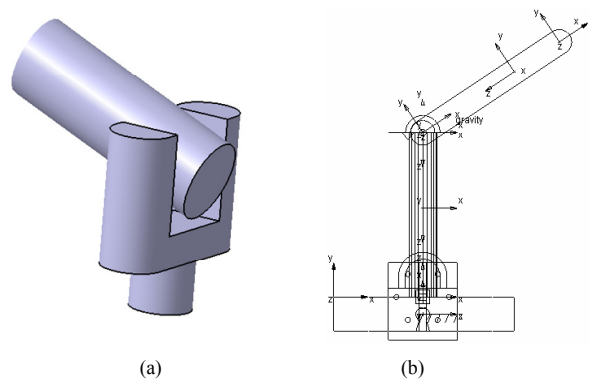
光电跟踪设备 CAD 模型 (a) 和动力学简化模型 (b)
